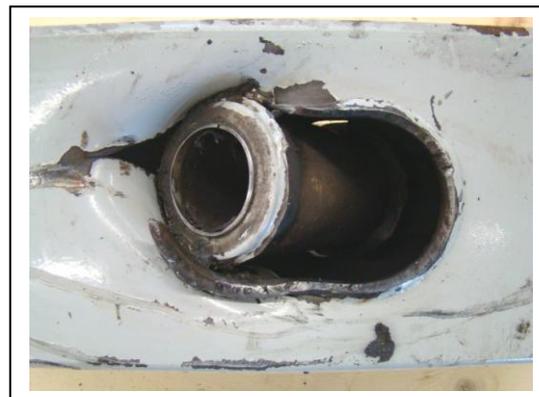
Bris dans la ZAT des soudures du manchon 3GI.
